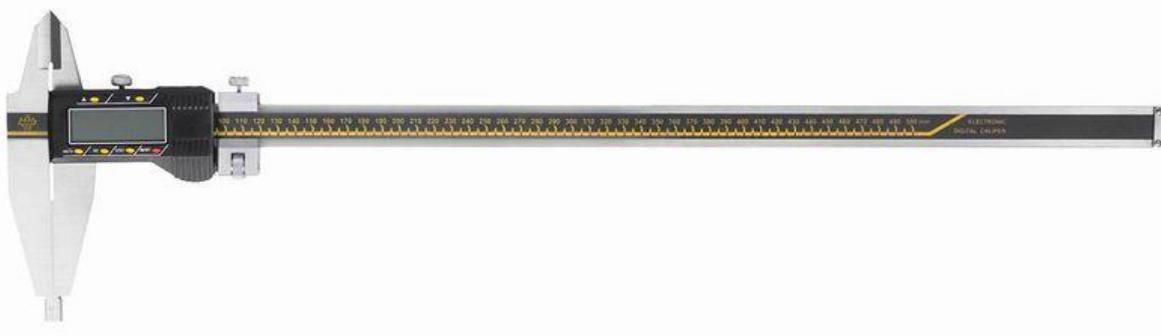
Общий вид штангенциркулей типа ШЦЦ-II
